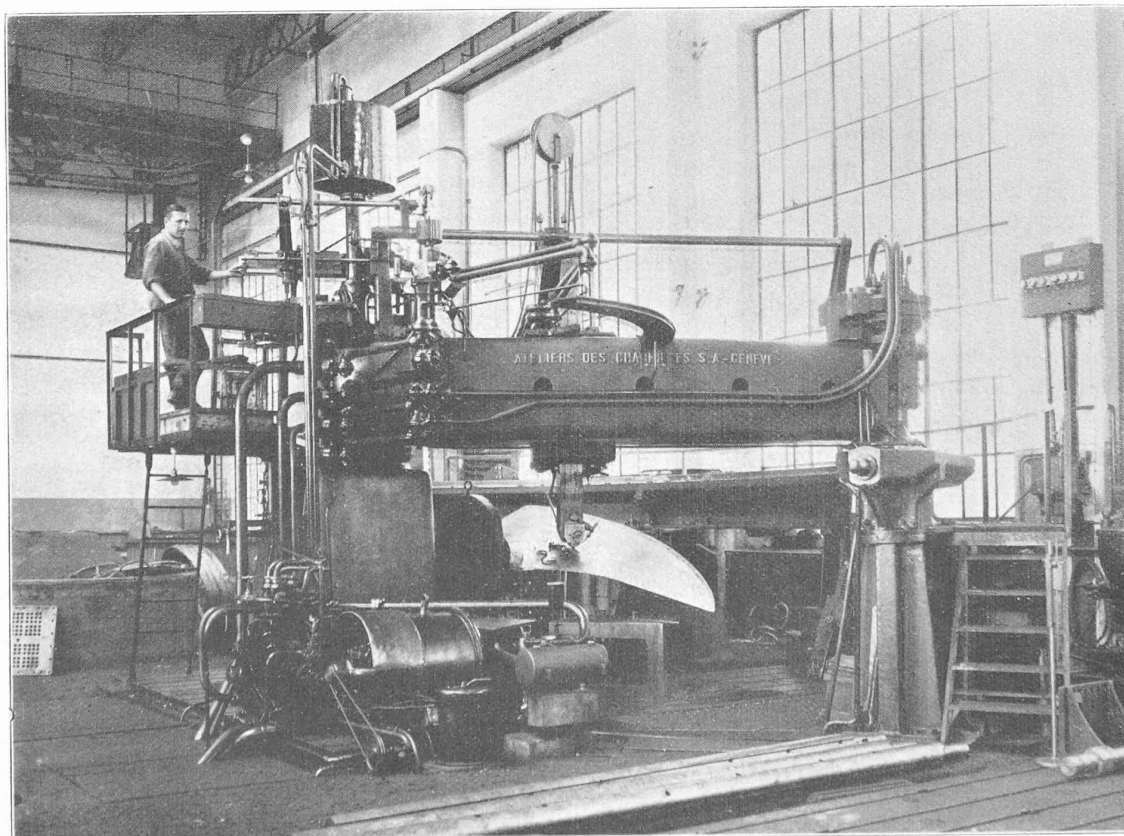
Vue de la machine à usiner les surfaces gauches.
